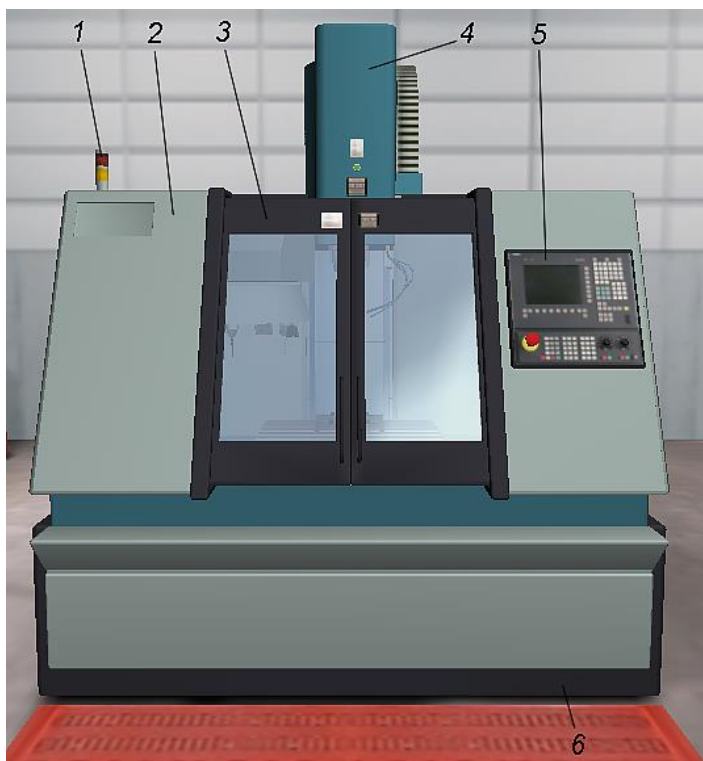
Общий вид универсального фрезерного центра [24]:
